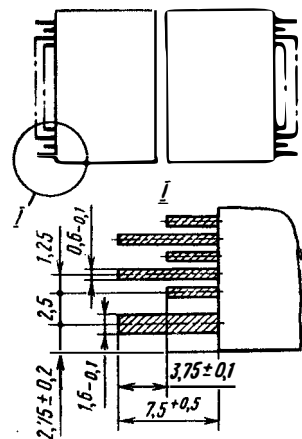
Гибкий печатный шлейф с двухрядным расположением контактных лепестков
